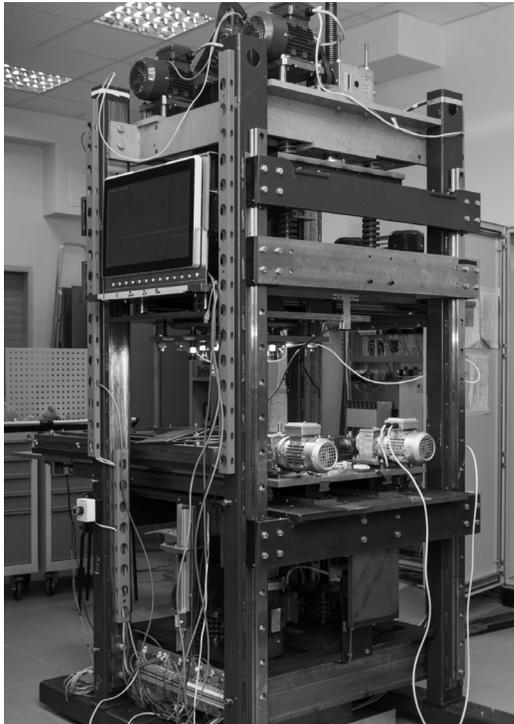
Общий вид установки фрикционной сварки «Странник»
